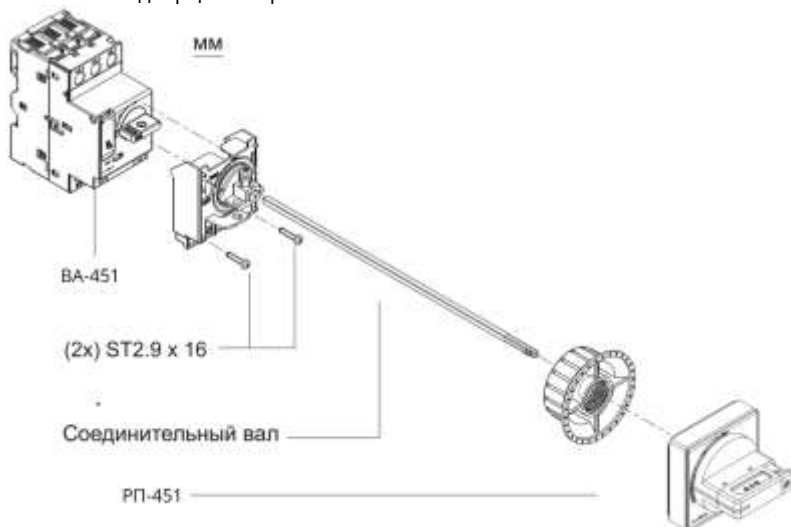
Схема установки рукояти на дверь шкафа РП-450
